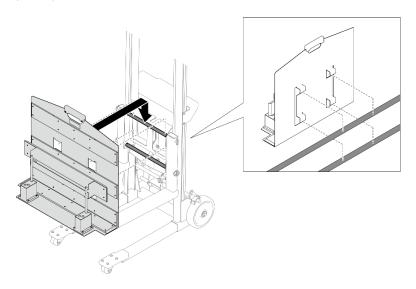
Fijación de la estructura de la herramienta de elevación sobre la herramienta de elevación
